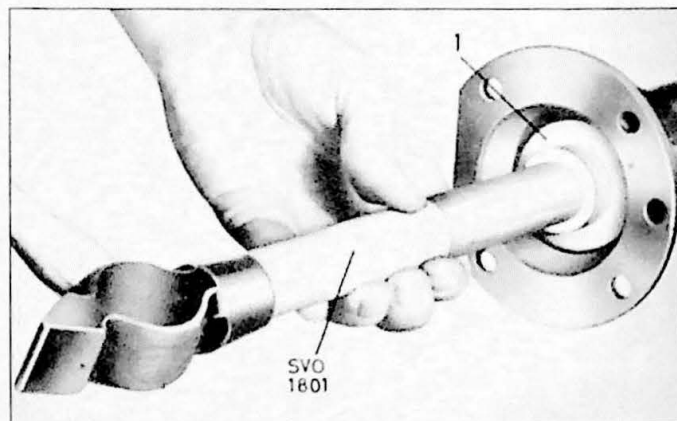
Montage viltring. 1. SVO 2456.
